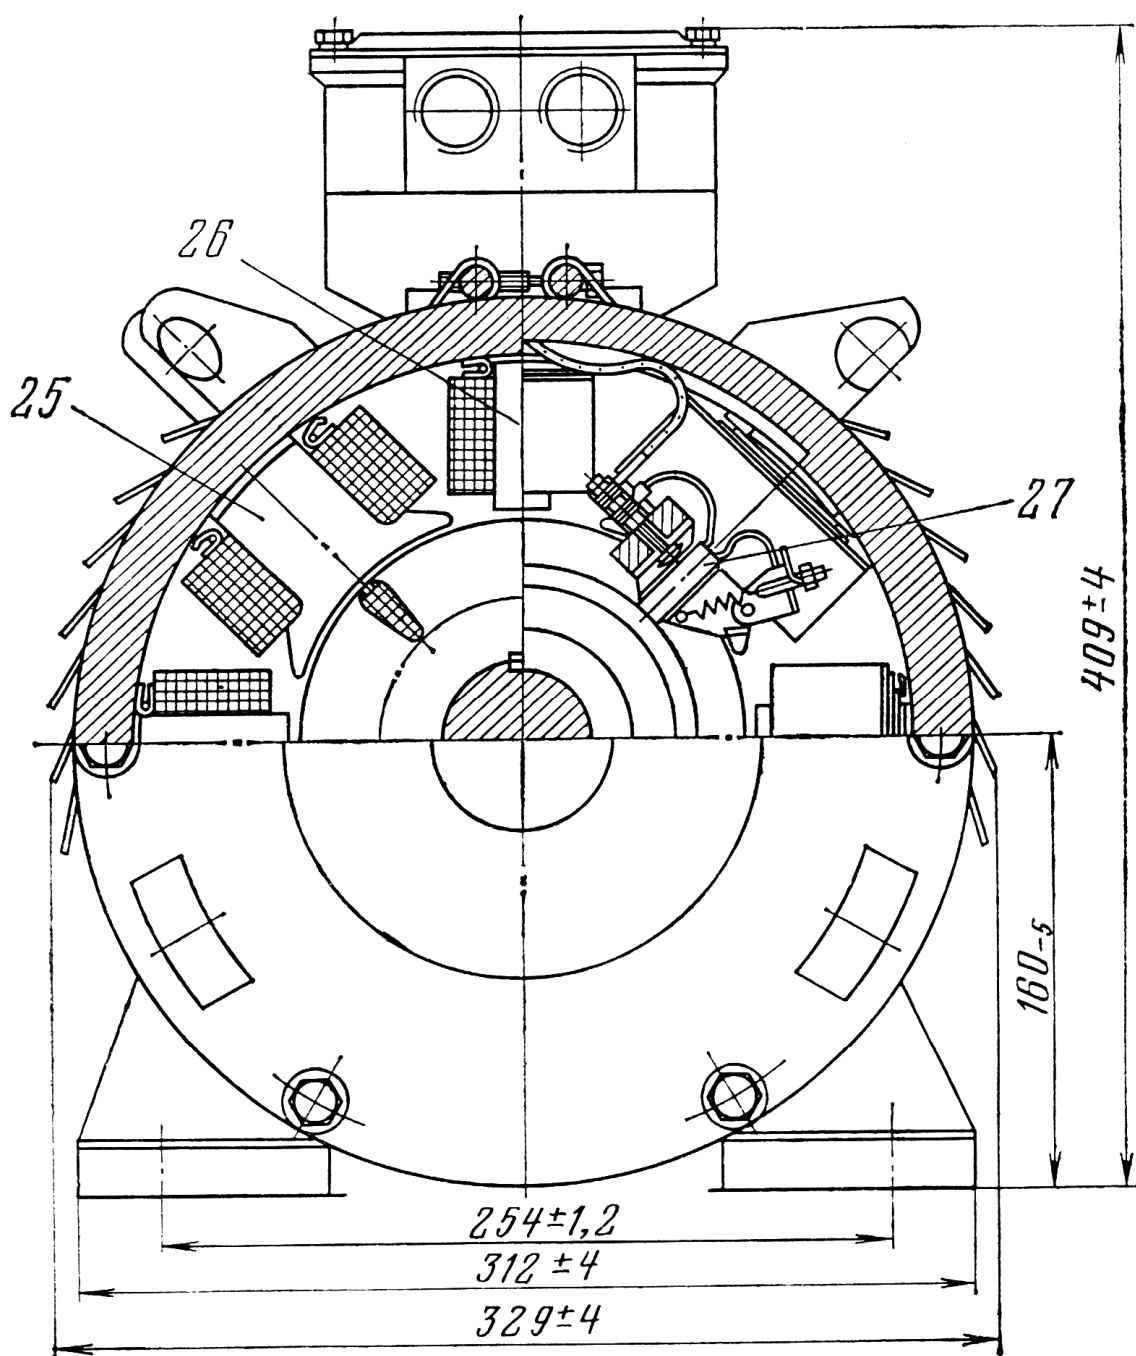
, а. Поперечний розріз двигуна типу 2ПН160МУ4, IP22
